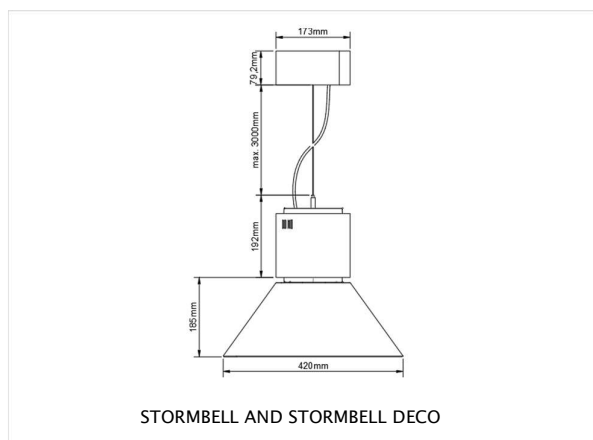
Exemple d'un schéma de rosace en aluminium pour une installation en saillie. (tableau 1) Sur les modèles STORBELL 173 et STORBELL DECO.
